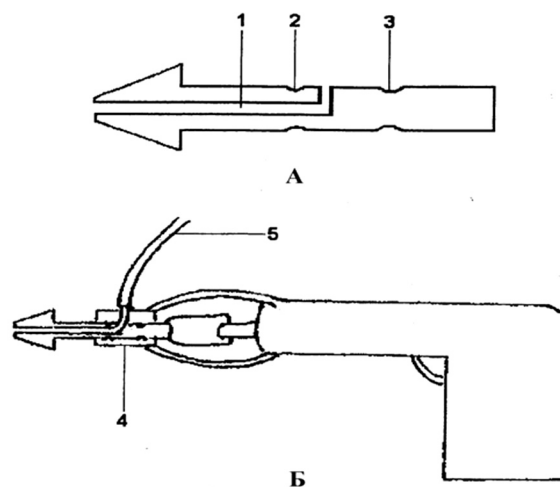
Внешний вид фрезы (А) и ее соединения с электродрелью (Б): 1 — воздушный канал; 2 и 3 — фиксирующие пазы; 4 — переходник, укрепленный на электродрели; 5 — патрубков, соединенный с кислородным баллоном.
